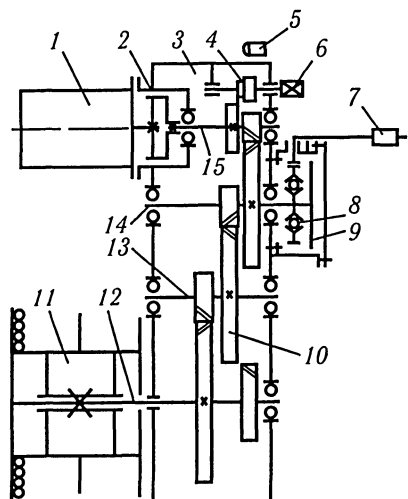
Кинематическая схема лебедки типа ЛШ:
